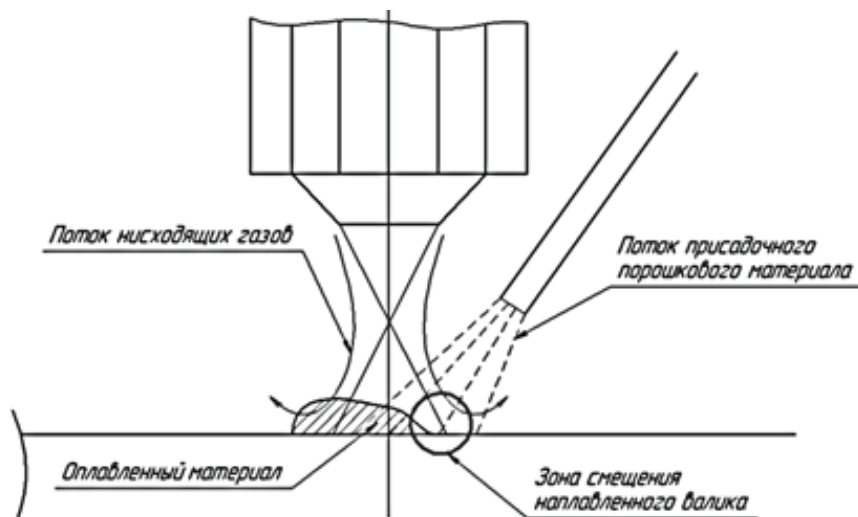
Схема процесса наплавки с боковой подачей порошкового материала
